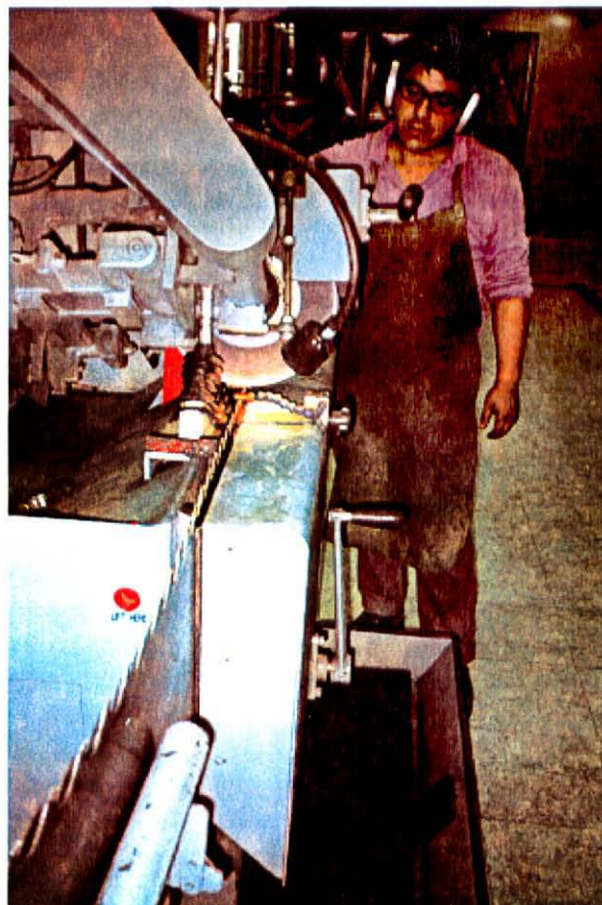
VISTA PARCIAL DE UNA AFILADORA DE CONSTRUCCIÓN ROBUSTA.
